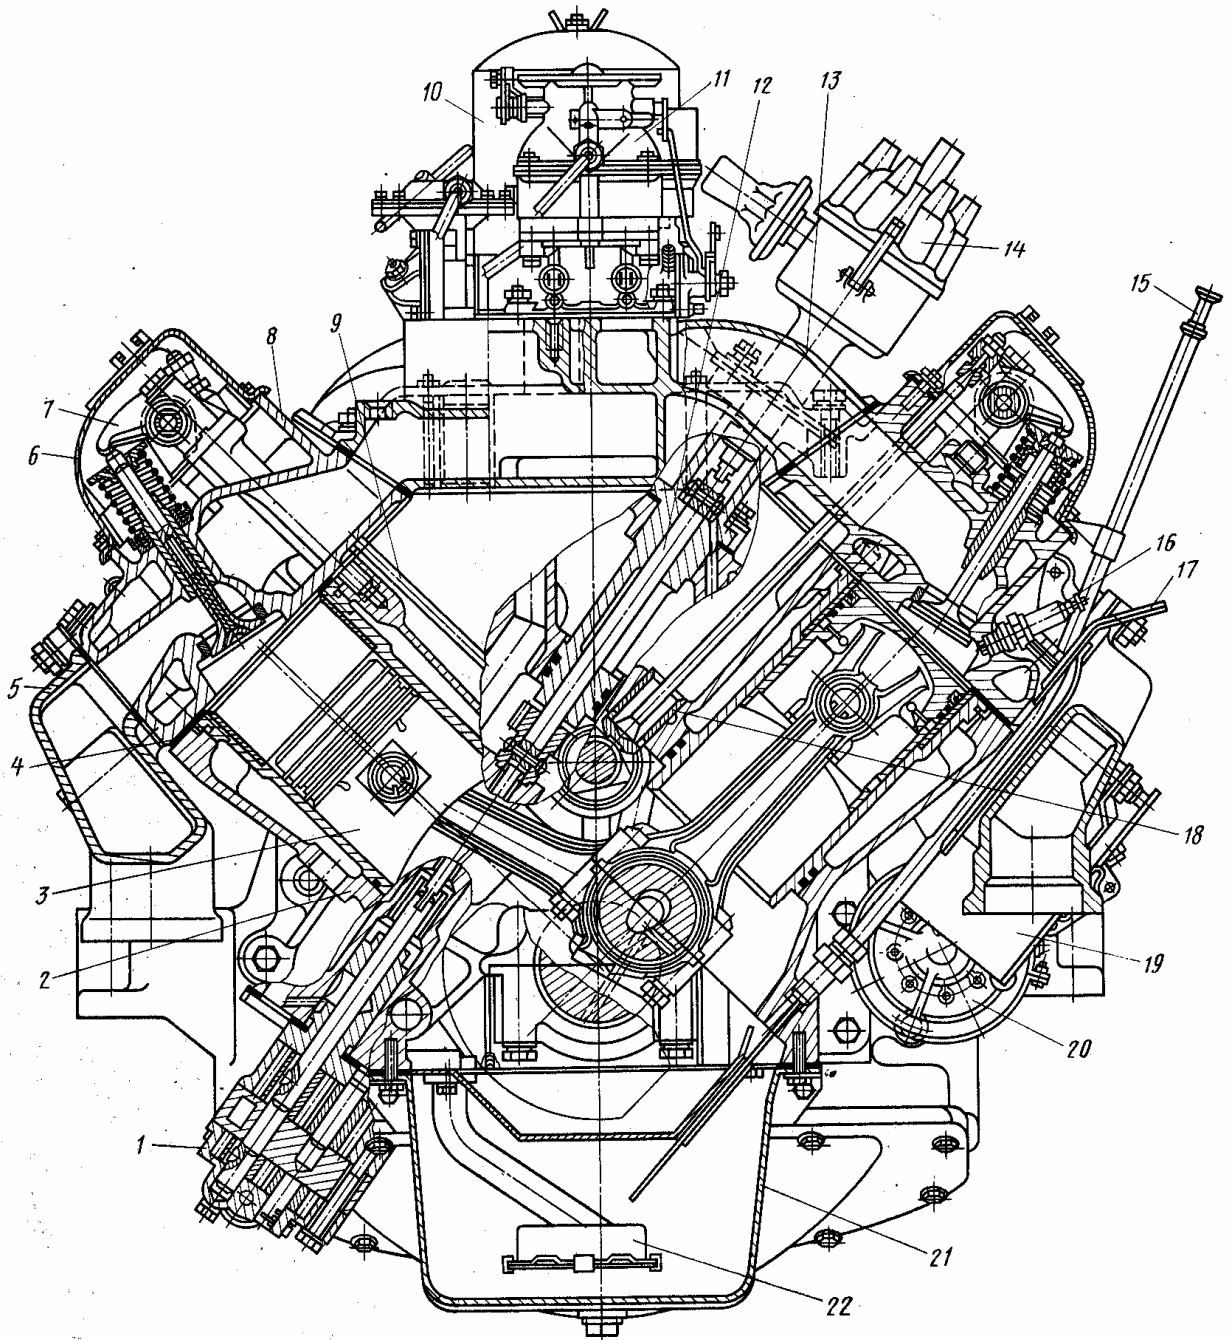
Поперечный разрез двигателя внутреннего сгорания: 1 – масляный насос; 2 – блок цилиндров; 3 – поршень с шатуном; 4 – прокладка головки цилиндров; 5 – коллектор выпускной; 6 – крышка коробки толкателей; 7 – коромысло; 8 – головка цилиндров; 9 – штанга коромысла; 10 – фильтр очистки масла; 11 – карбюратор; 12 – валик привода распределителя; 13 – труба впускная; 14 – распределитель зажигания; 15 – указатель уровня масла; 16 – свеча зажигания; 17 – защитный щиток свечей; 18 – толкатель; 19 – щиток стартера; 20 – стартер; 21 – масляный картер; 22 – маслоприемник
